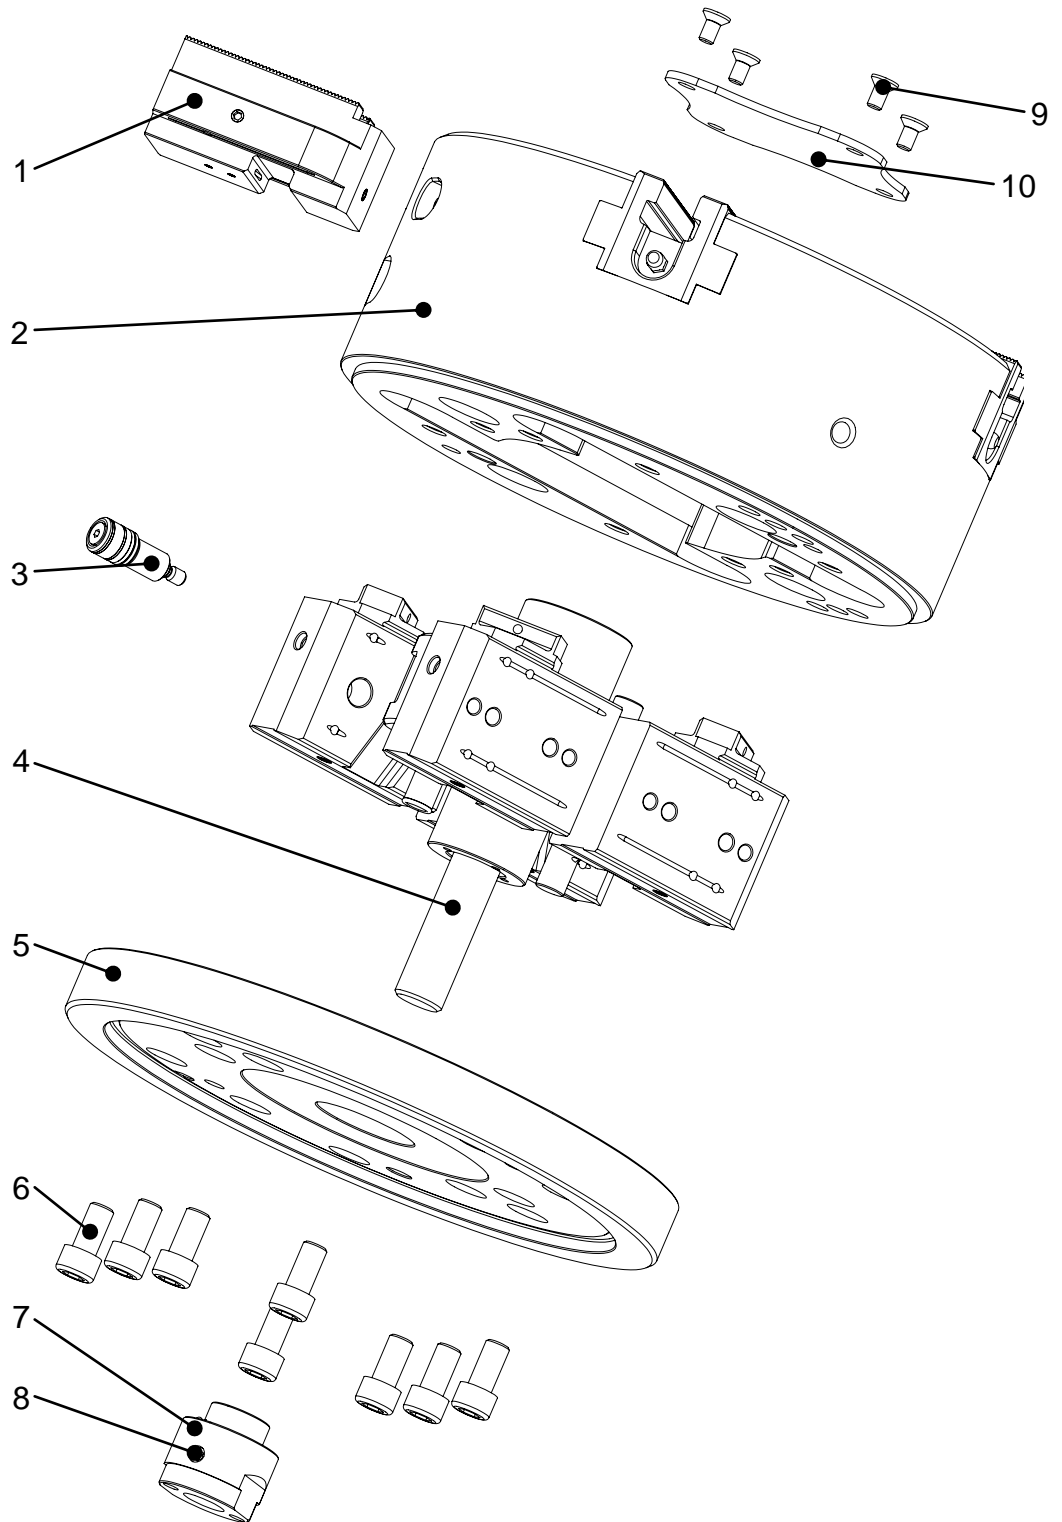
desmontaje / montaje del mandril (VK021 - VK080)
